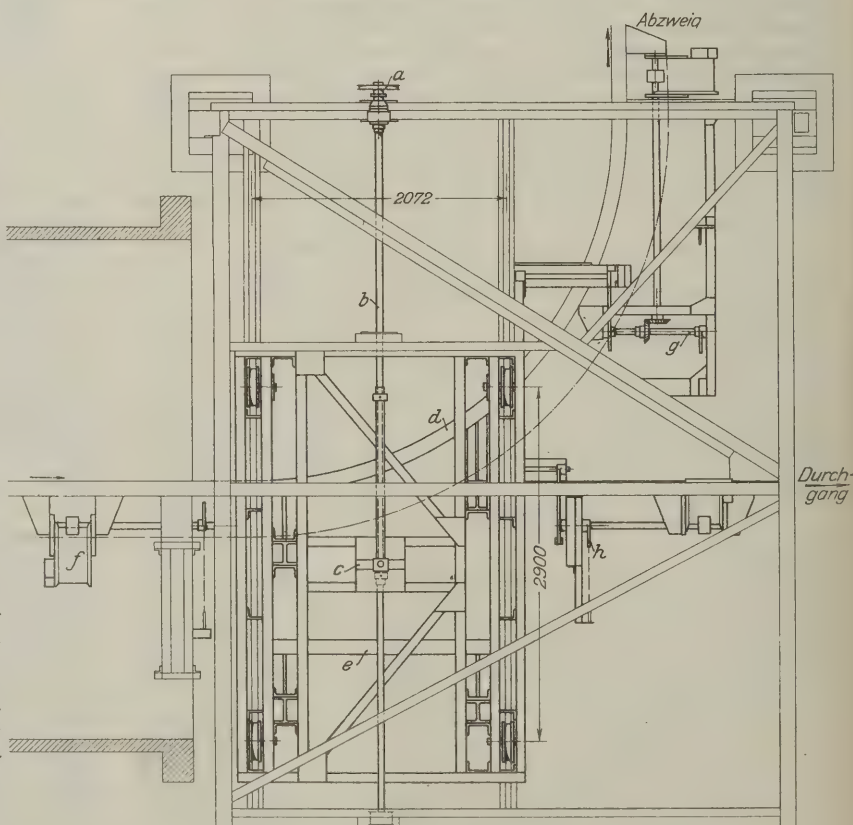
Grundriß einer Schiebeweiche mit Fahrbahnverriegelung.
